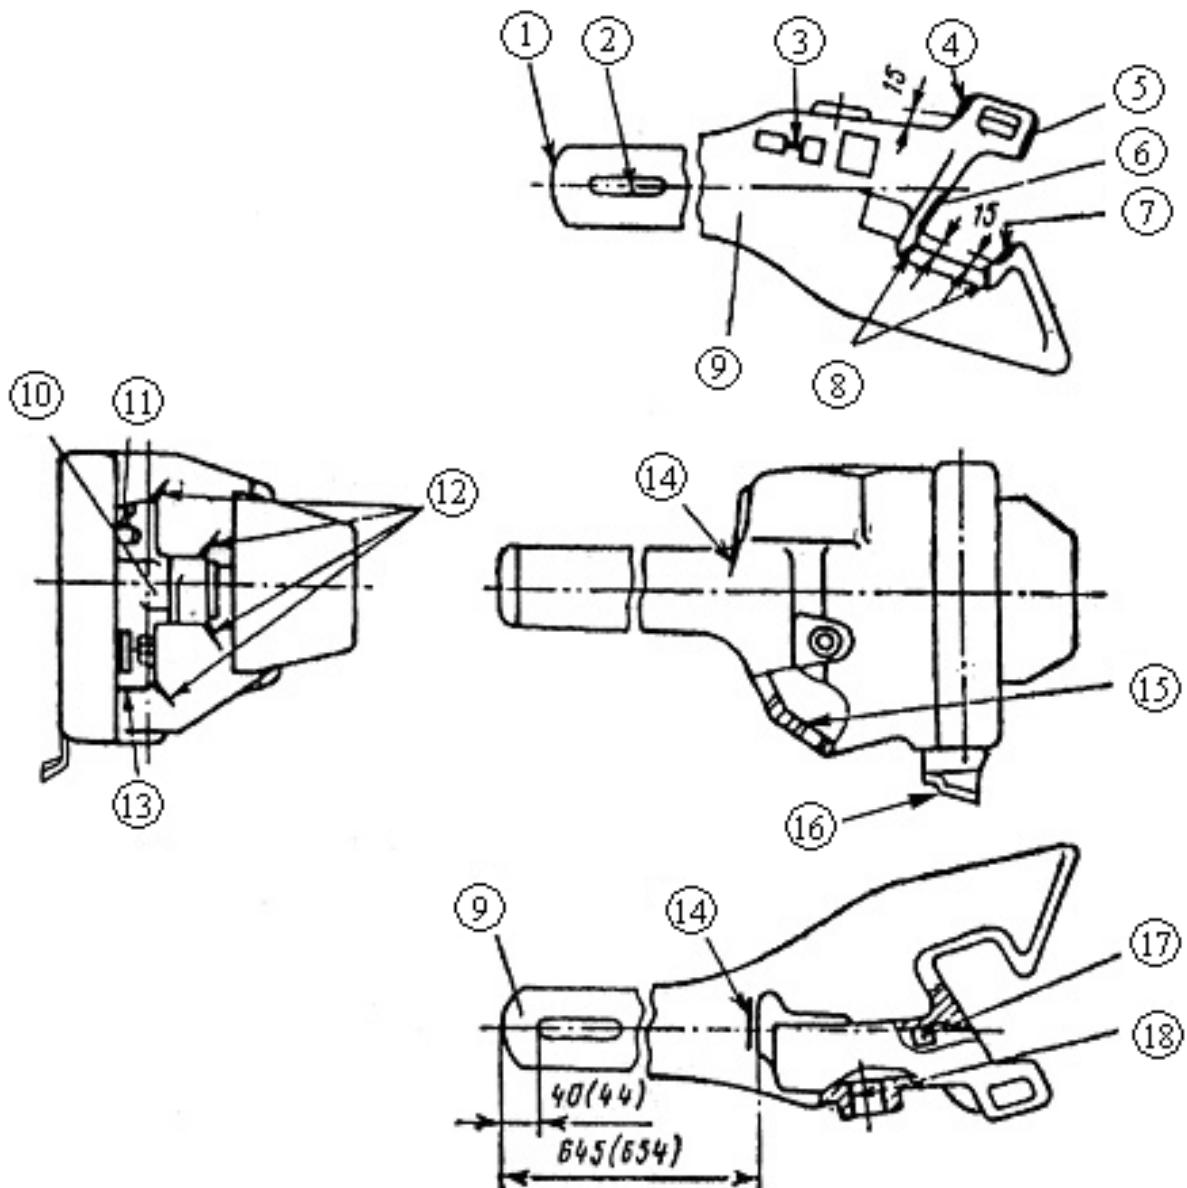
Дефекты корпуса автосцепки, ремонтируемые сваркой или наплавкой
